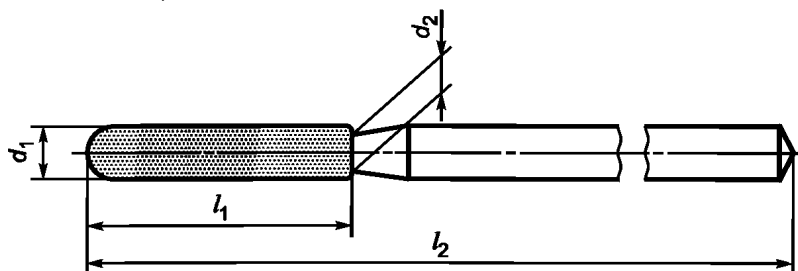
Цилиндрическая полусферическая рабочая часть с длиной головки 10,0 мм
